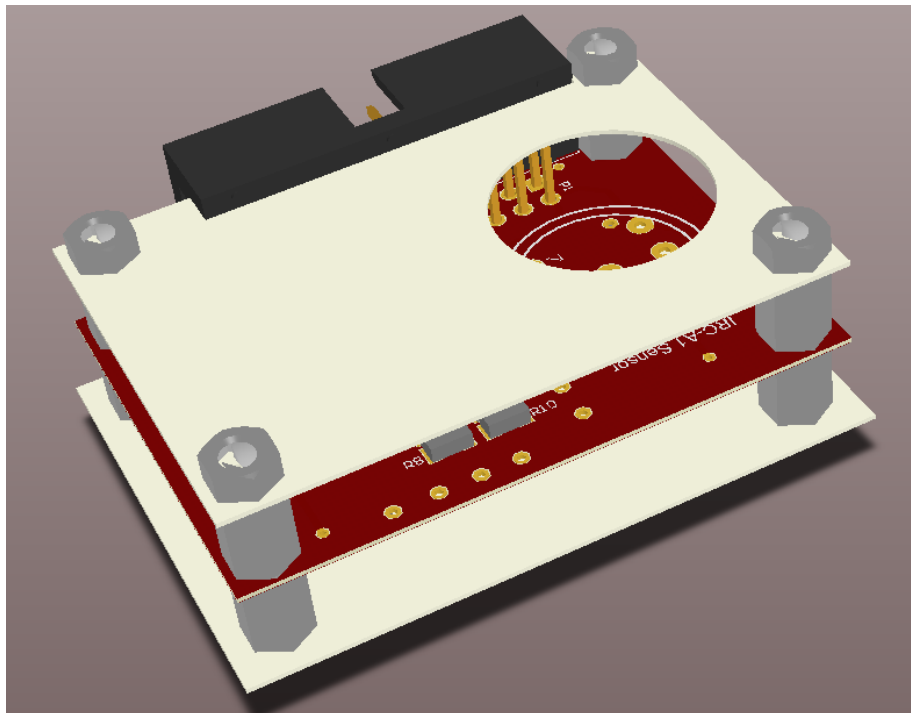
Υλοποίηση PCB αισθητήρων_1
